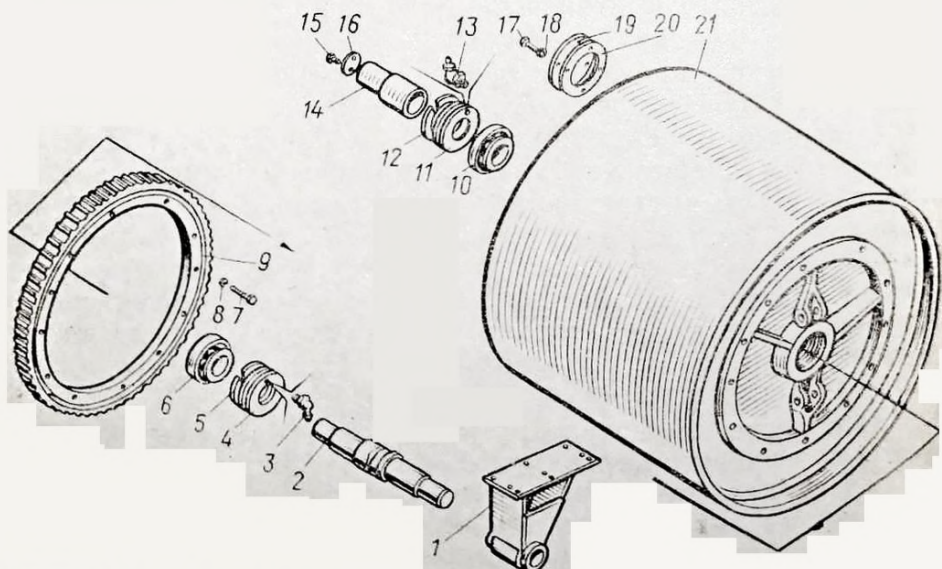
Задний ведущий валец катка ДУ-49А
